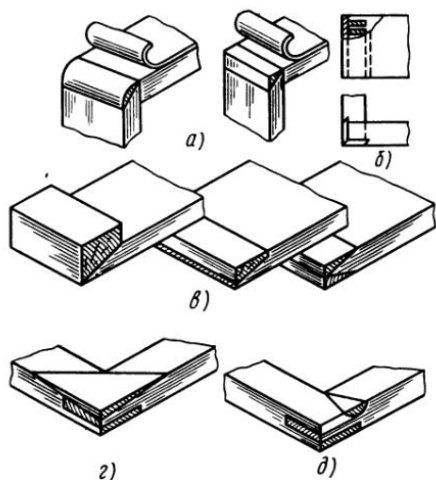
Заделка торцовых поверхностей деталей и сборочных единиц из массивной древесины:
